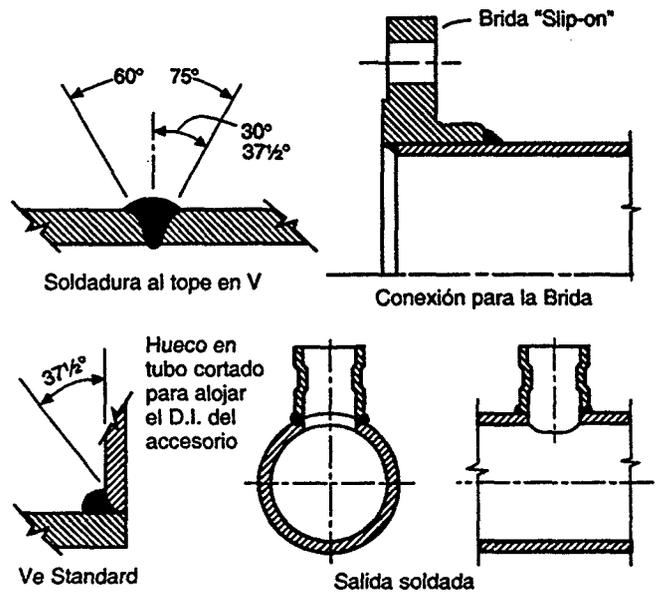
(a) Juntas Soldadas aceptables
